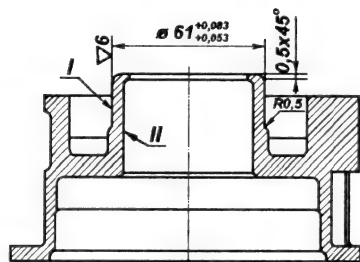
Посадочная поверхность картера, подготовленная для запрессовки кольца
